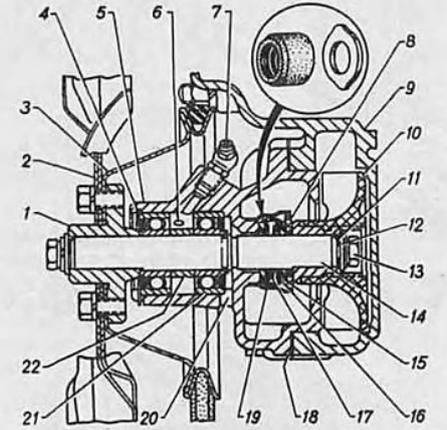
Водяной насос двигателя «Волга»: 1 — ступица; 2 — вентилятор; 3 — шкив; 4 — стопорное кольцо; 5 — корпус; 6 — контрольное отверстие для выхода смазки; 7 — пресс-масленка; 8 — уплотняющая шайба; 9 — кронштейн насоса; 10 — крыльчатка; 11 — резиновая шайба; 12 — шайба; 13 — болт; 14 — валик водяного насоса; 15 — манжета сальника; 16 — обойма пружины; 17 — пружина; 18 — прокладка; 19 — держатель сальника; 20 — контрольное отверстие выхода воды; 21 — подшипник; 22 — распорная втулка.
